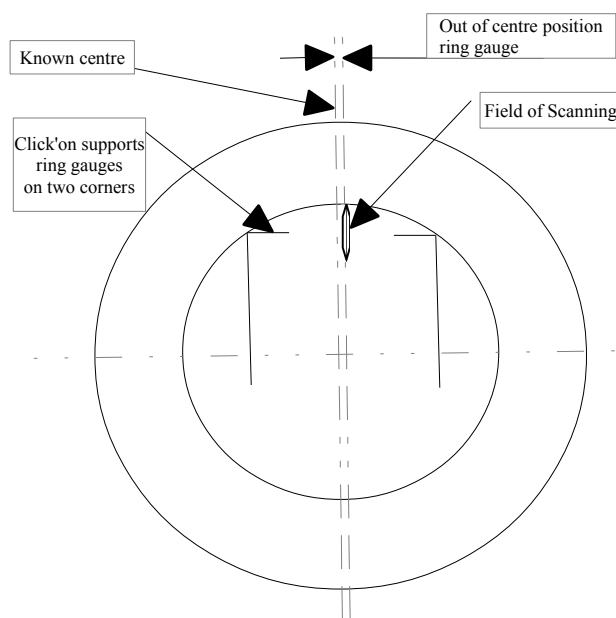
Промежуточная калибровка поддержки с калиброванными установочными кольцами
